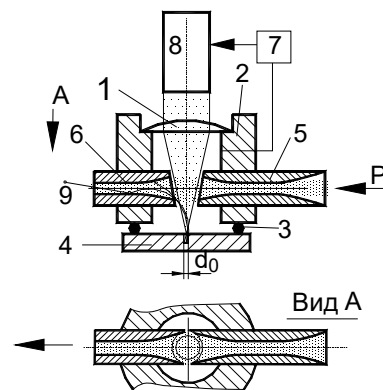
Схема пристрою для лазерної прецизійної обробки отворів з використанням ежекторного ефекту: 1 – лінза, 2 – корпус, 3 – ущільнення, 4 – заготівка, 5 – плоске сопло для наддуву газу, 6 – приймальне сопло для випуску газу, 7 – блок керування лазером, 8 – лазер, 9 – продукти ерозії
